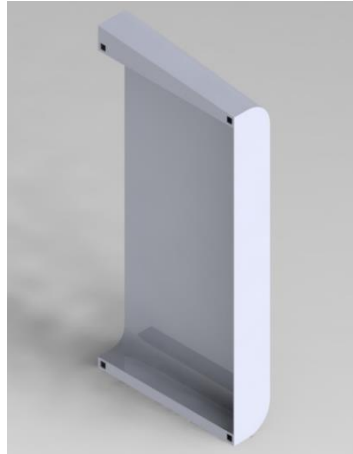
Ensamblaje subconjunto 1.1. Soldadura 13 y 14.
